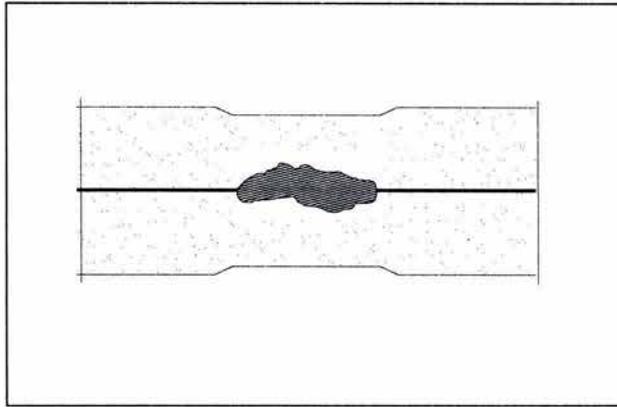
Soldadura incorrecta, mecánicamente débil debido a que la zona de fusión es muy pequeña.
